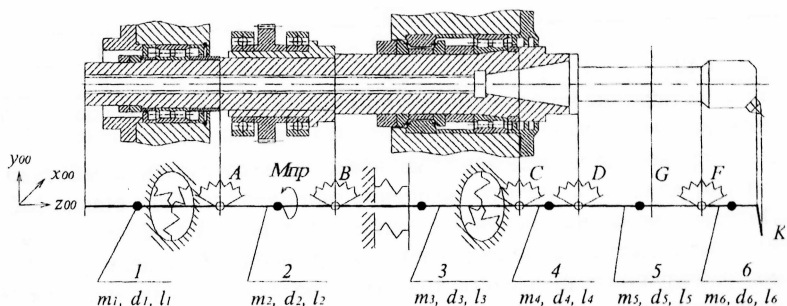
Конструктивная и расчетная схема ШУ станка MC12-250
